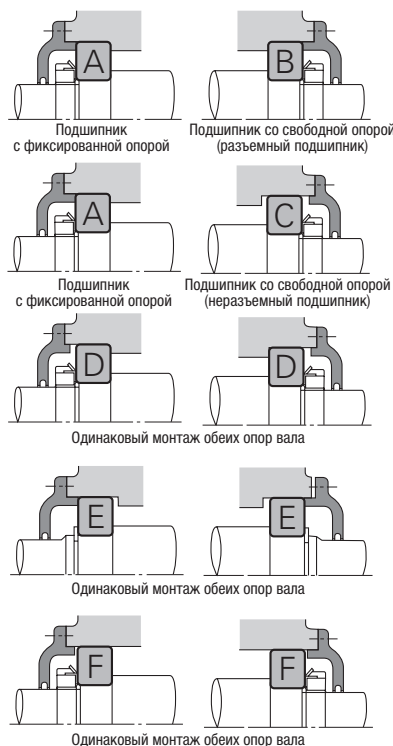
Выбор типа подшипника и способы монтажа
